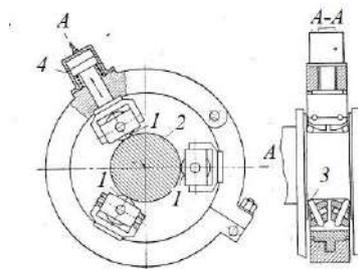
Схема упрочнения галтелей (1 – ролики; 2 – шейка коленчатого вала; 3 – галтели вращающегося коленчатого вала; 4 – гидроцилиндр)
